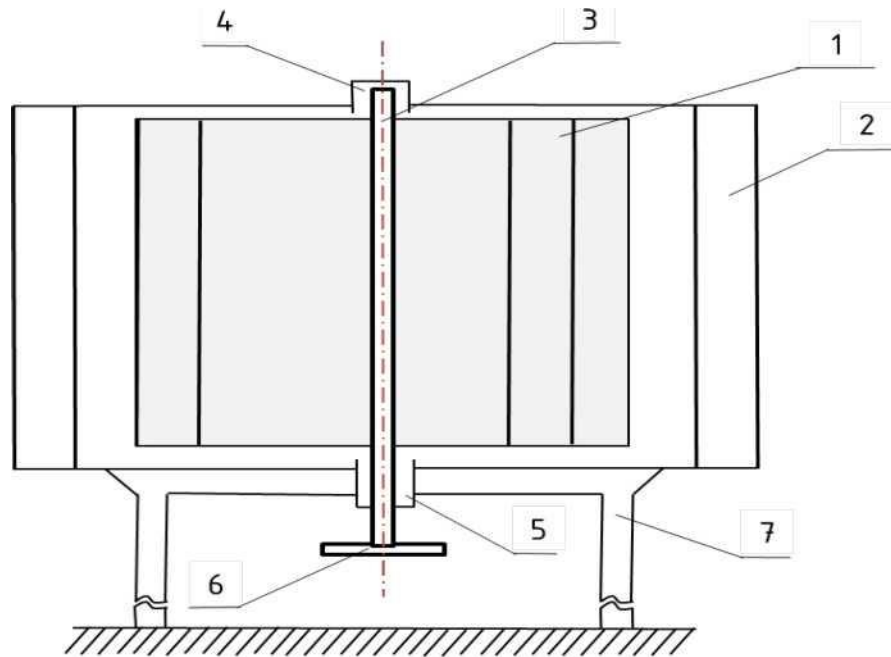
Вертикально-осьовий вітроваго двигун багатолопатєвого типу 1 - ротор із лопатями; 2 - напрямляючі лопаті статора; 3 - вал; 4 - підшипниковий вузол, що центрує; 5 - опорний підшипниковий вузол; 6 - з'єднувальна муфта для передавання механічної енергії обертання електрогенератору; 7 - рама (основа)
